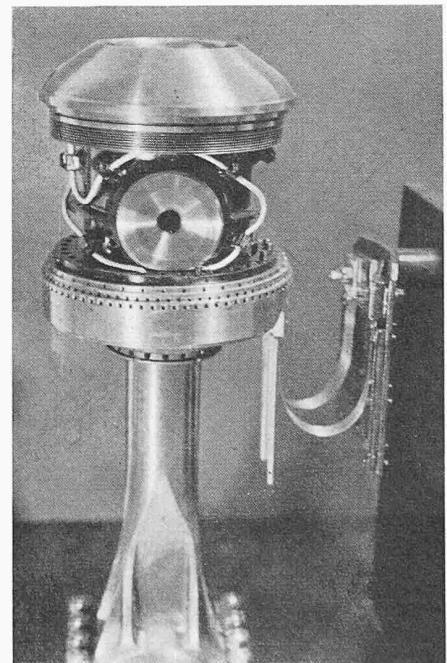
(rechts). Herausführung der Drähte für Thermo-
